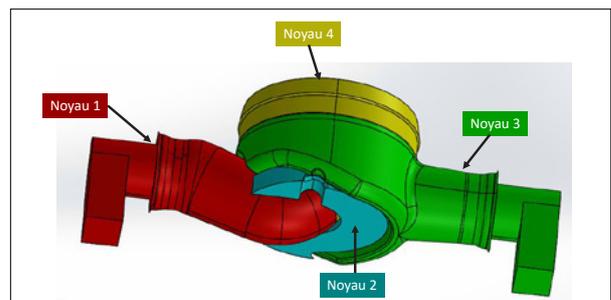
Vue de l'assemblage des noyaux extrait de l'étude de moulage
